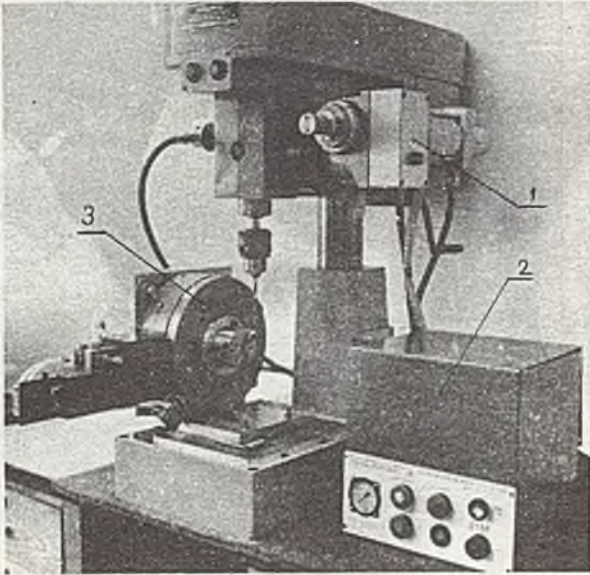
przedstawia zestaw z cylindrem pneumo-hydraulicznym realizujący ruch automatyczny: "szybki dobieg - ruch roboczy - szybkie wycofanie" /symbol ZWO/.
